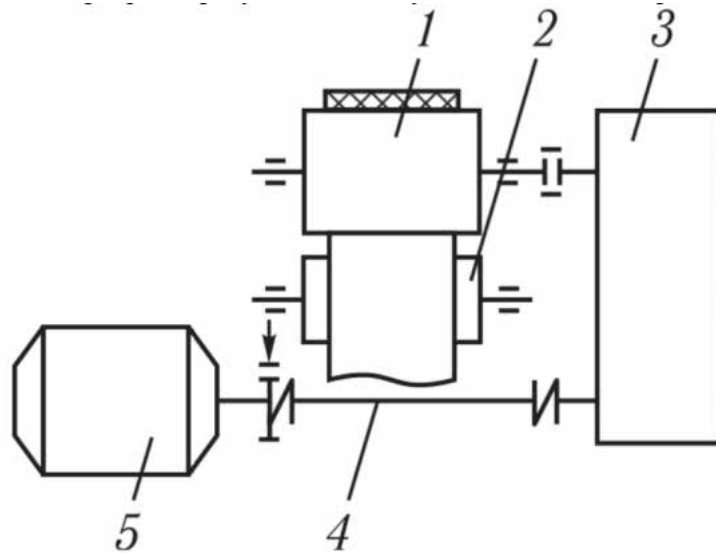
Схема приводного пристрою стрічкового конвеєра 1 - приводний барабан; 2 - відхильний барабан; 3 - редуктор; 4 - проміжний вал; 5 - електродвигун
